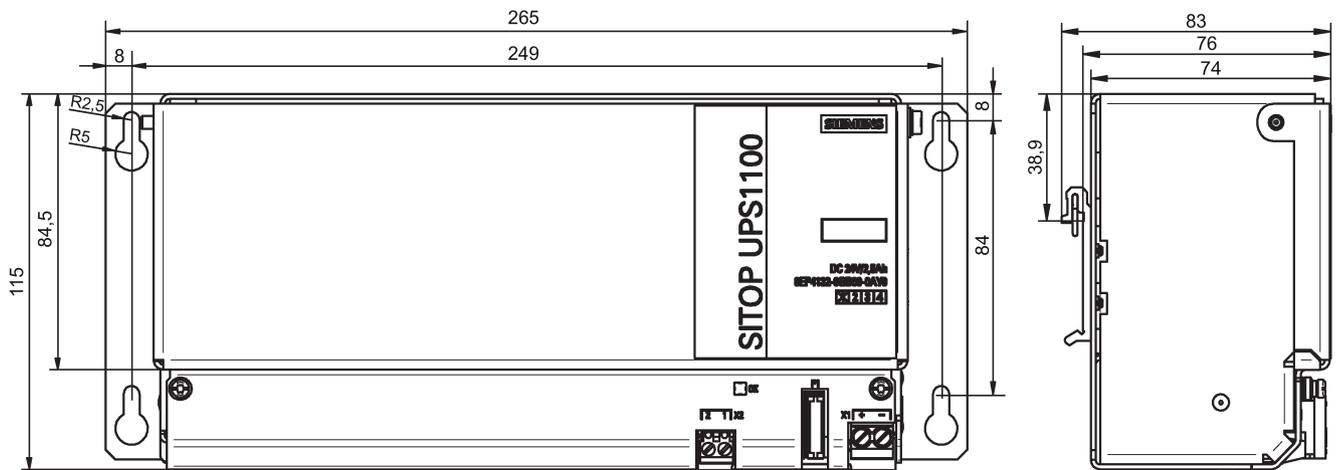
Maßzeichnung 6EP4132-0GB00-0AY0
